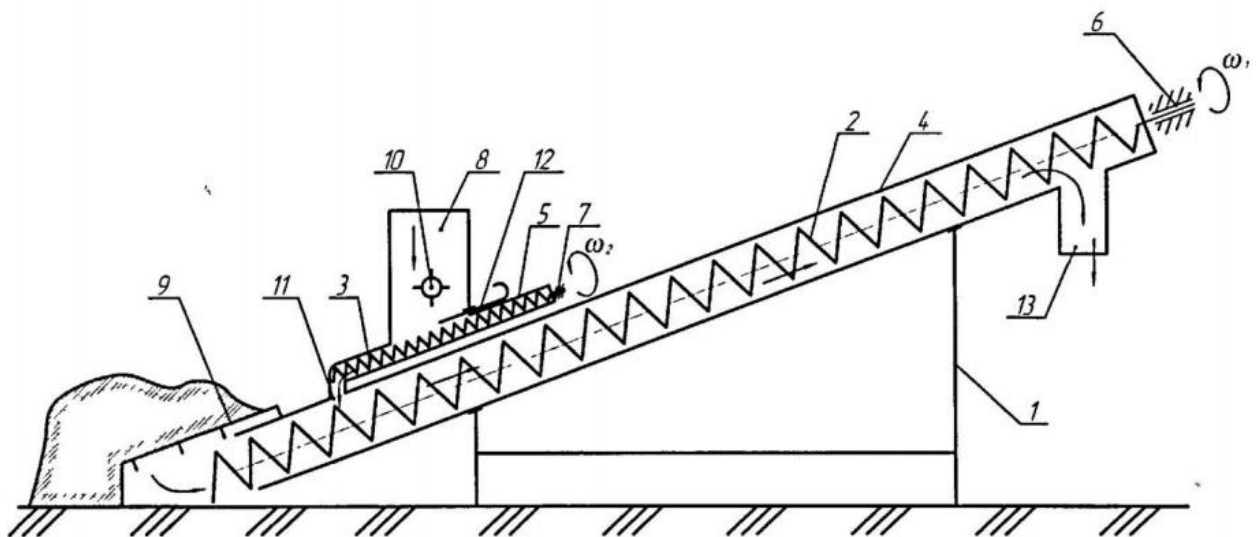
Дозатор-змішувач сипучих матеріалів: 1 – рама; 2 - робочий орган більшого діаметра; 3 - робочий орган меншого діаметру; 4,5 – кожухи; 6,7 – приводи; 8 – бункер; 9 - захисна решітка; 10 – ворушилка; 11 – патрубок; 12 - заслінка; 13 - вивантажне вікно
